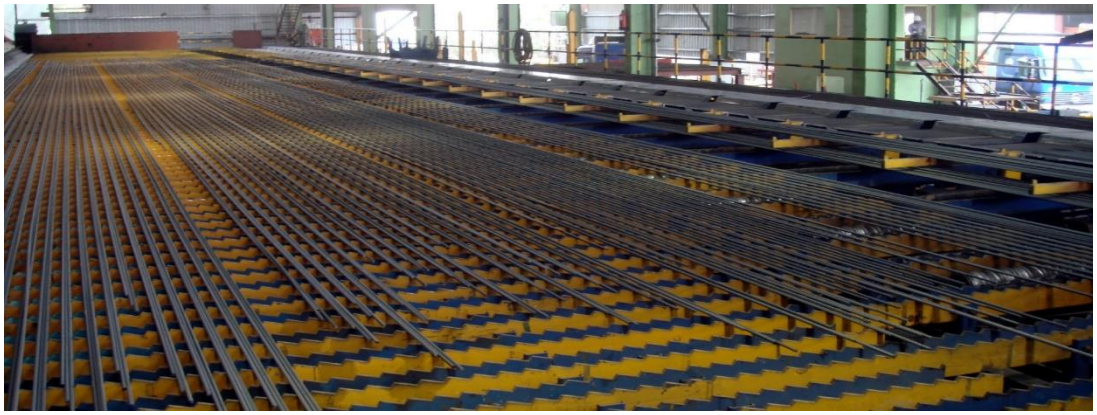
Загальний вид рейкового холодильника сортового стану
